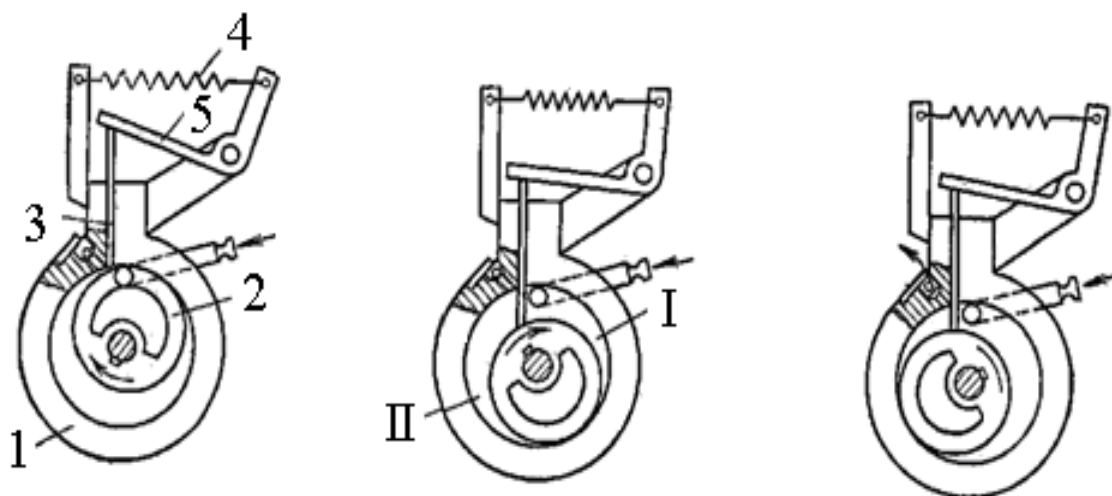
Пластинчато – статорные насосы: 1 - цилиндрическая камера; 2 – эксцентрично расположенный ротор, 3 – пластина, 4 – пружина; 5 – рычаг.
